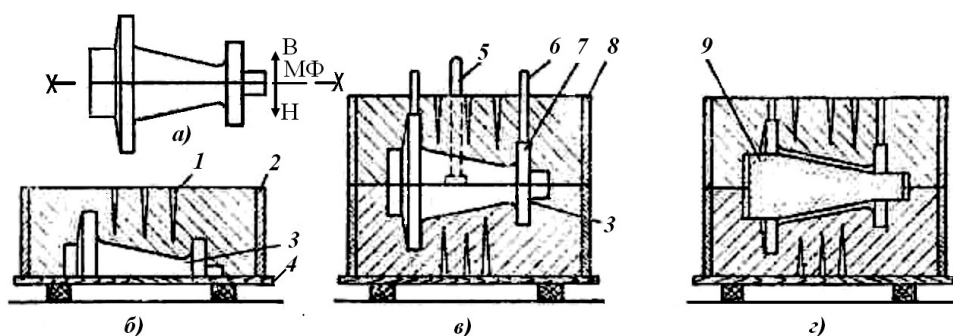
Изготовление формы в двух опоках по разъемной модели
